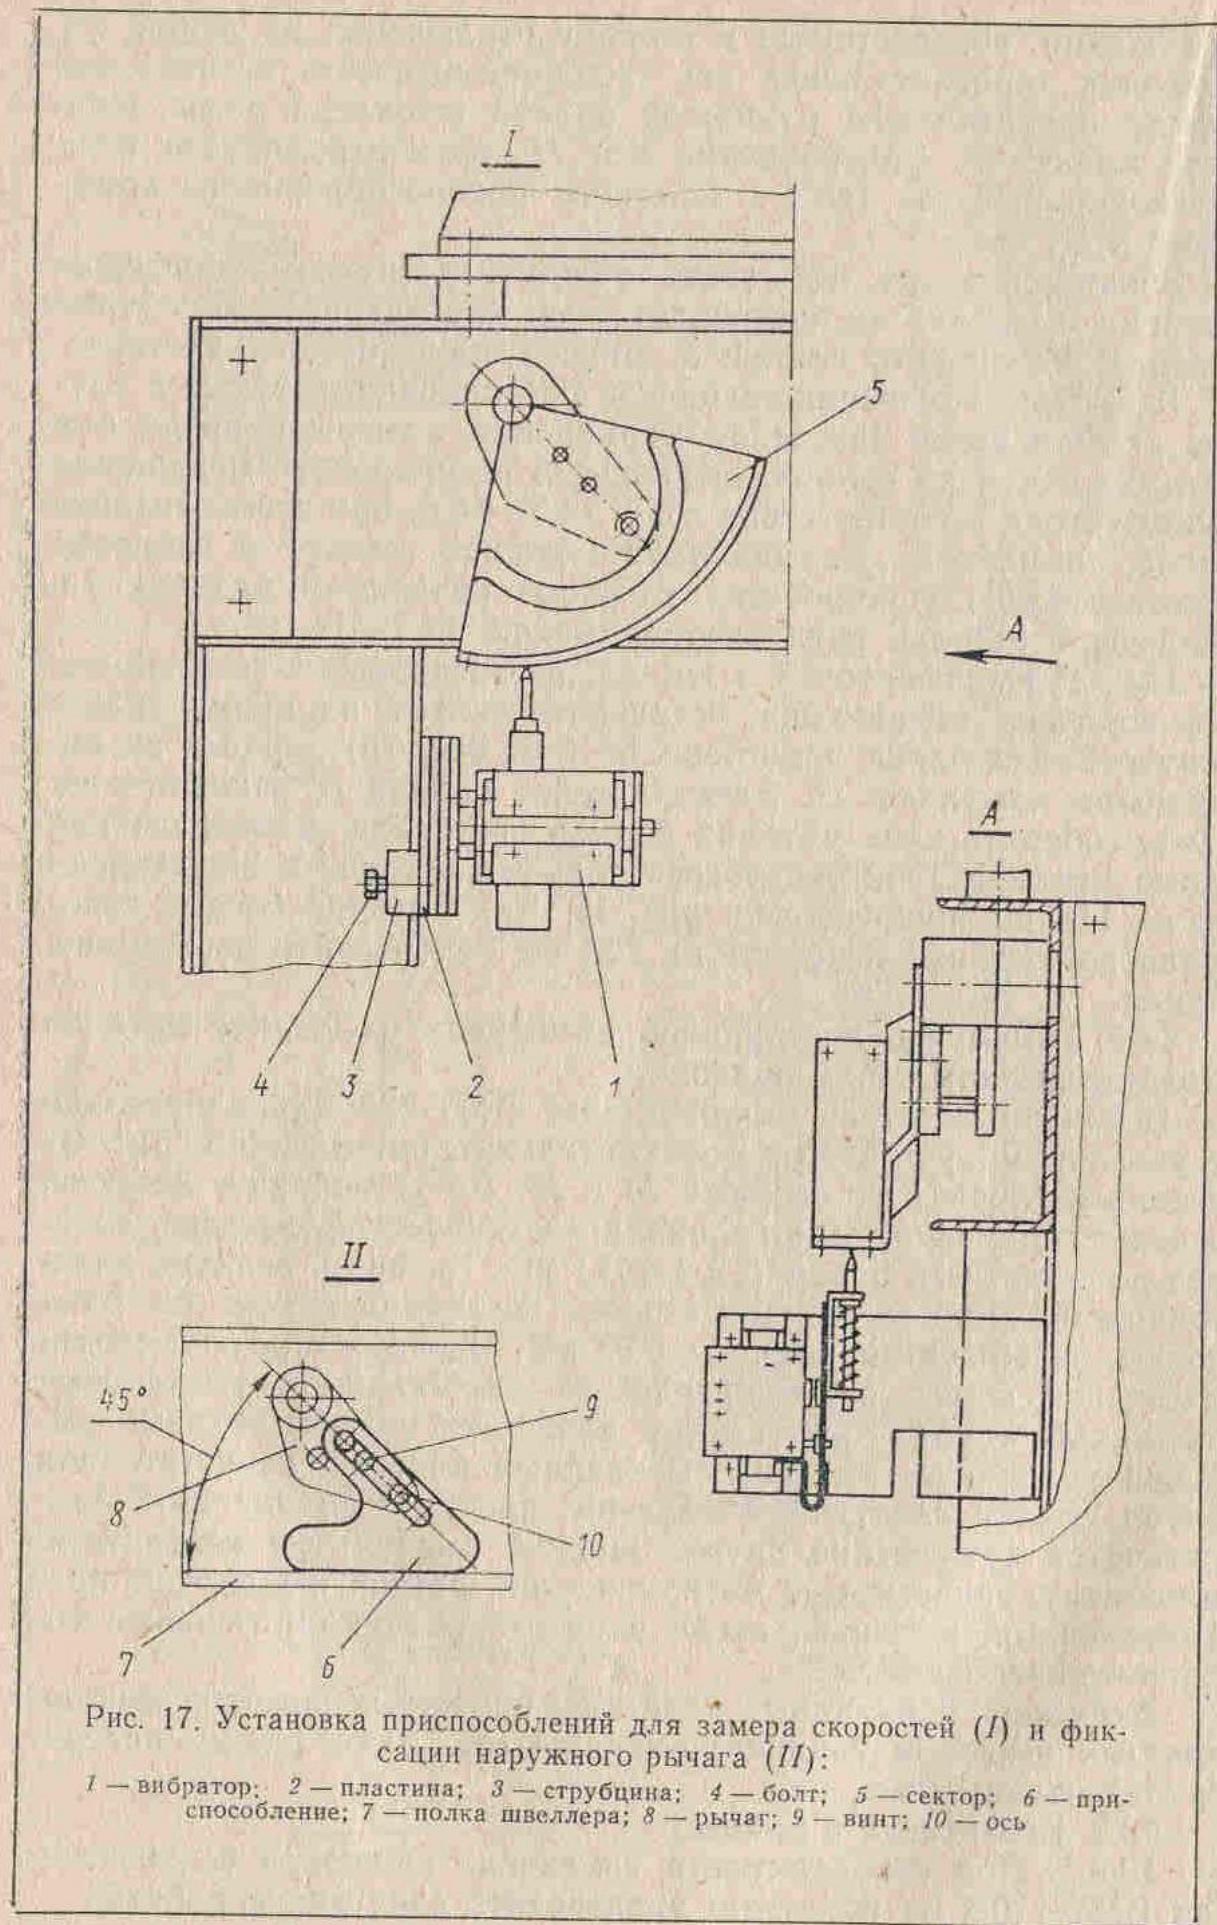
Установка приспособлений для замера скоростей (I) и фиксации наружного рычага (II):
